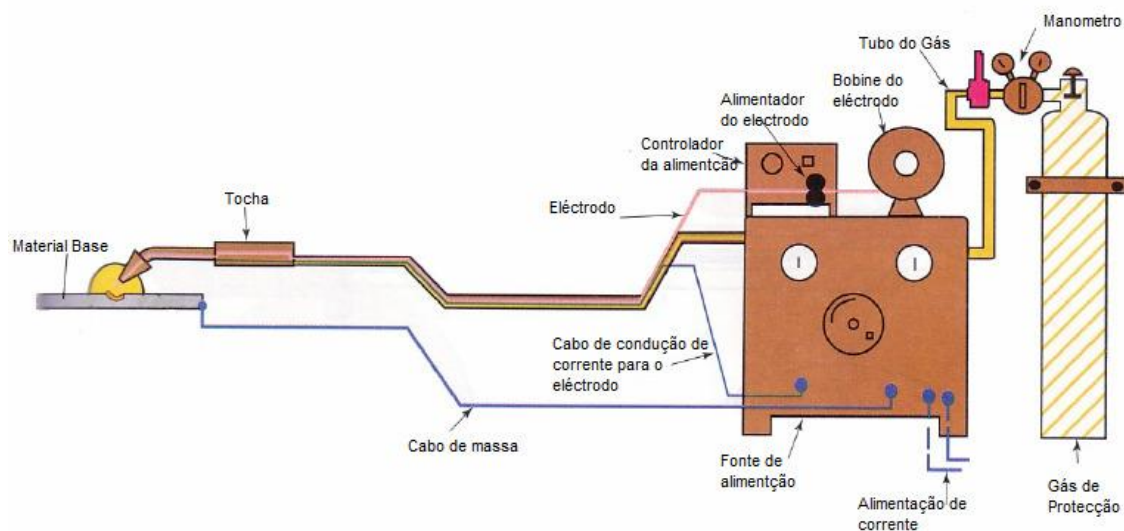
Esquema dum equipamento de soldadura MIG/MAG
